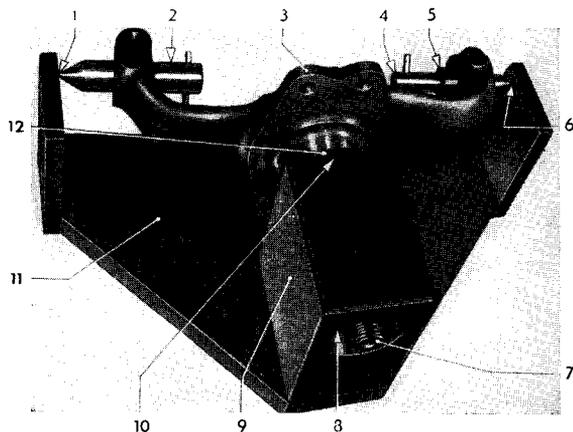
Prüfung des Achsschenkels mit oberer Kugelgelenklagerung und unterem Achsschenkelagerzapfen
